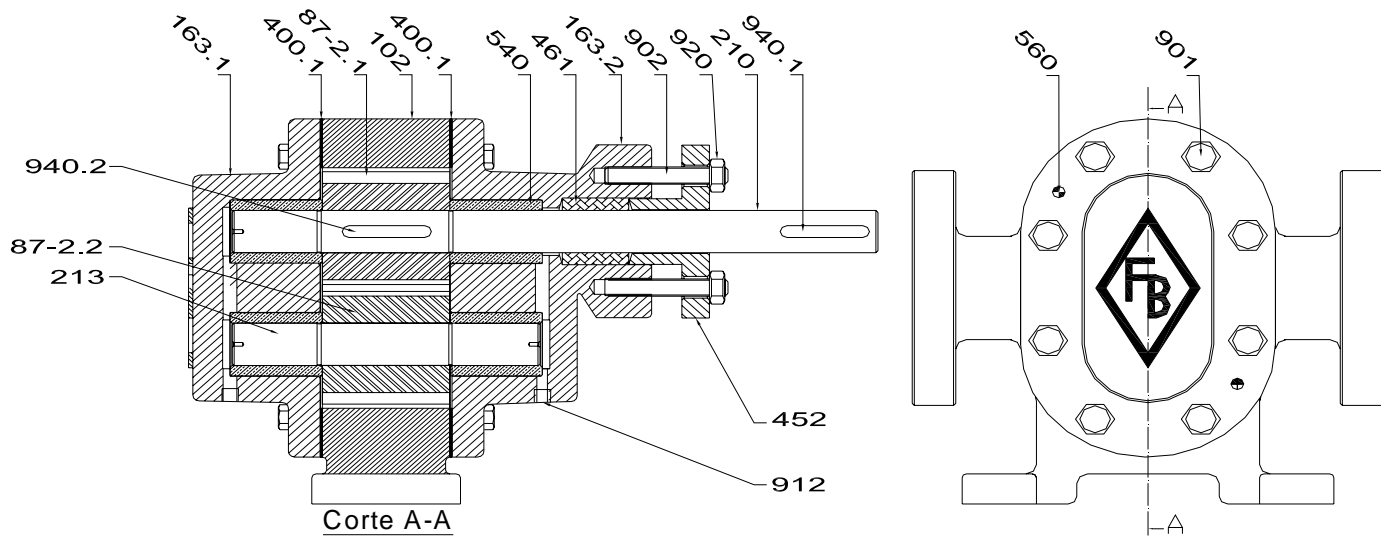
Desenho em Corte bomba FBE 1.1/2” – 2” – 3” com gaxeta
